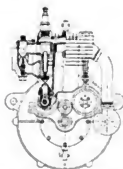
Dürkopp-Vierzylindermotor, Querschnitt.
